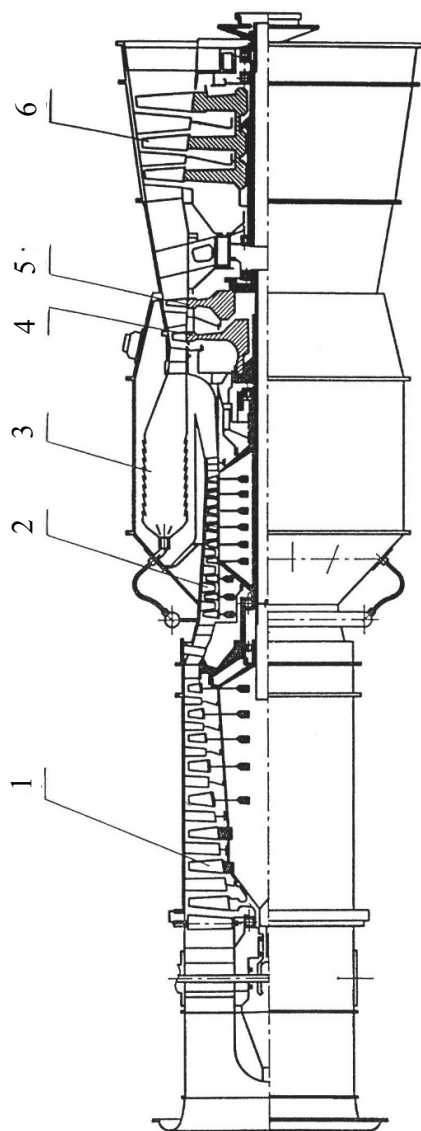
Конструктивная схема ГТД ДТ71П:
